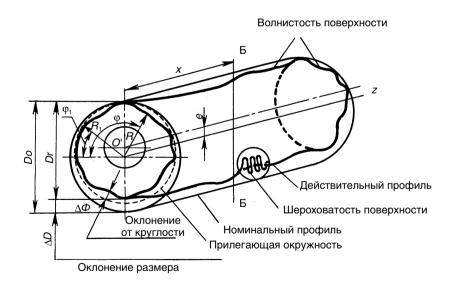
Отклонения геометрической поверхности цилиндрической детали
